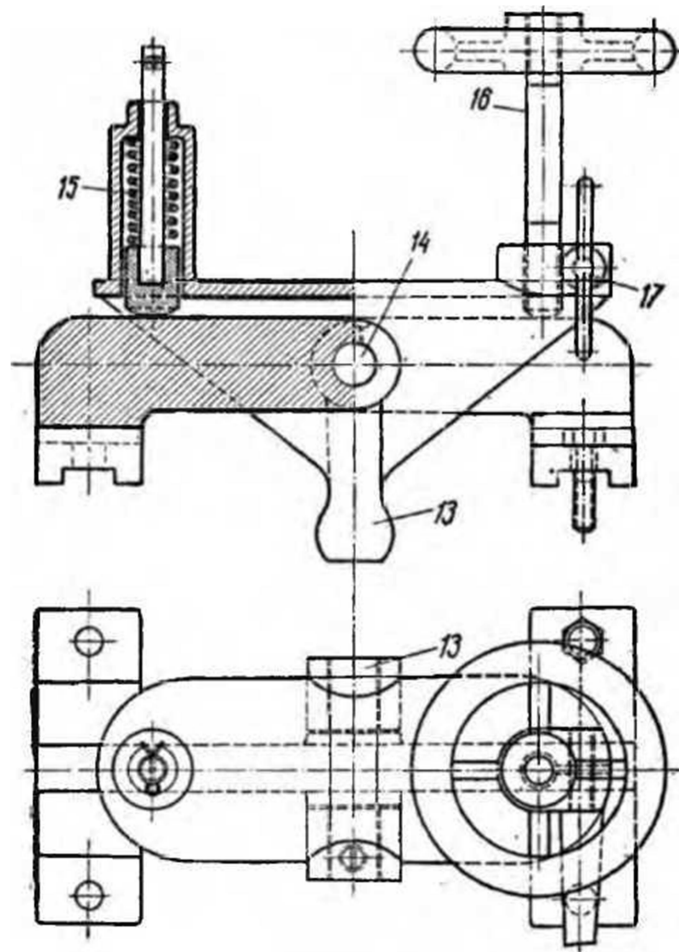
Механізм для автоматичного регулювання величини зазору між дисками
